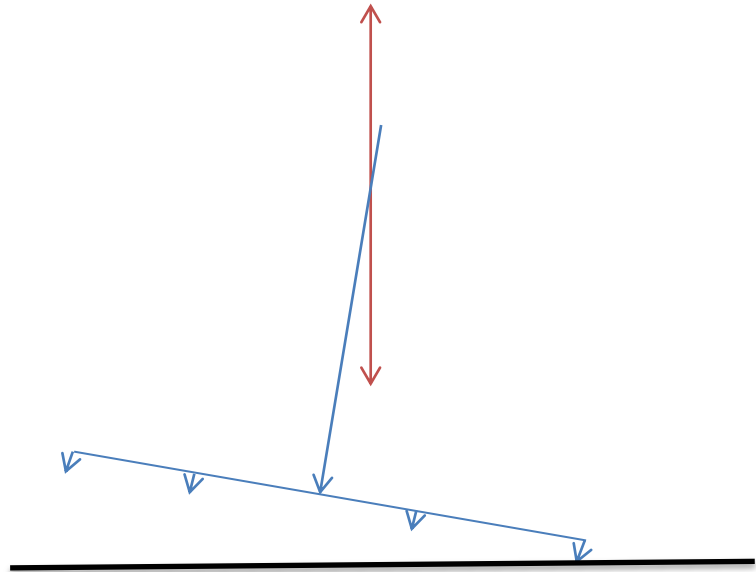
Fehler Spindelachse - Werkzeugachse
